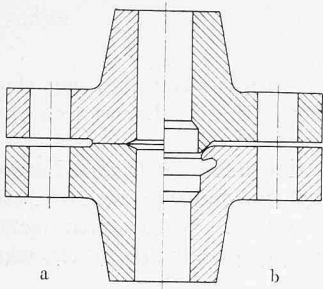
Flanschverbindung für hohe Temperaturen. a Ausführung nach DIN 2548, b Ausführung nach New Pipe Joints Challenge Welding Flanges. «Power» 115 (1971), Nr. 1, S. 76/77
